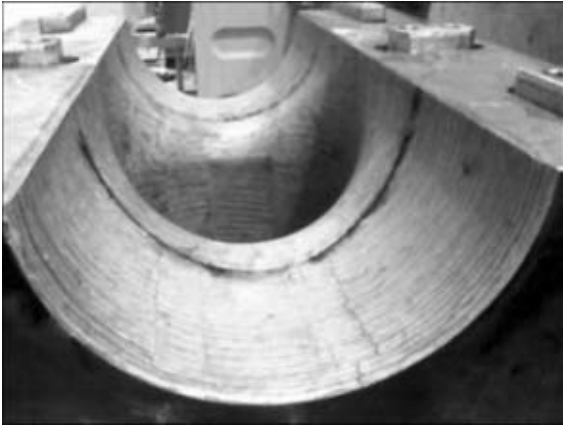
Матрица для формовки трубных тройников большого диаметра после плазменной закалки
